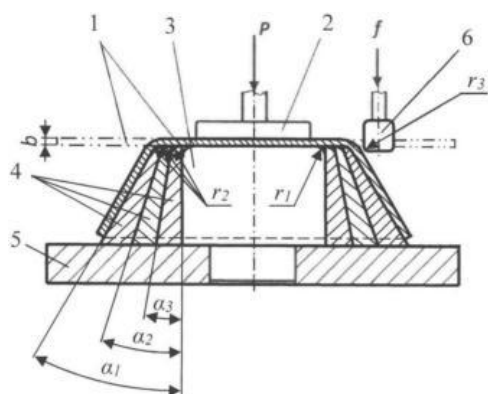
Многопереходная обкатка с применением конических элементов: 1- листовая заготовка ; 2- прижим; 3- оправка; 4- технологические конусные насадки; 5- корпус; 6- деформирующий ролик
